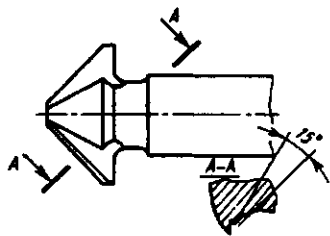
Зенковка с конической поверхностью стружечных канавок
